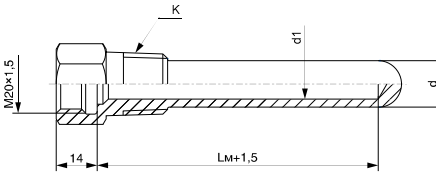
ГТ-702 цилиндрическая с конической резьбой для ДТ с подвижным штуцером
